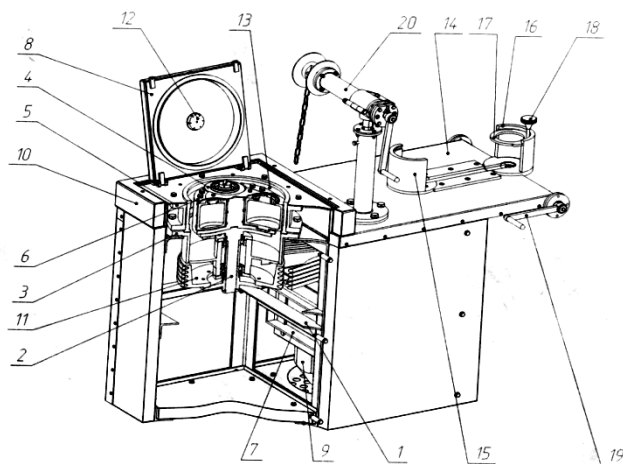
Внешний вид и устройство механоактиватора АГО-3
